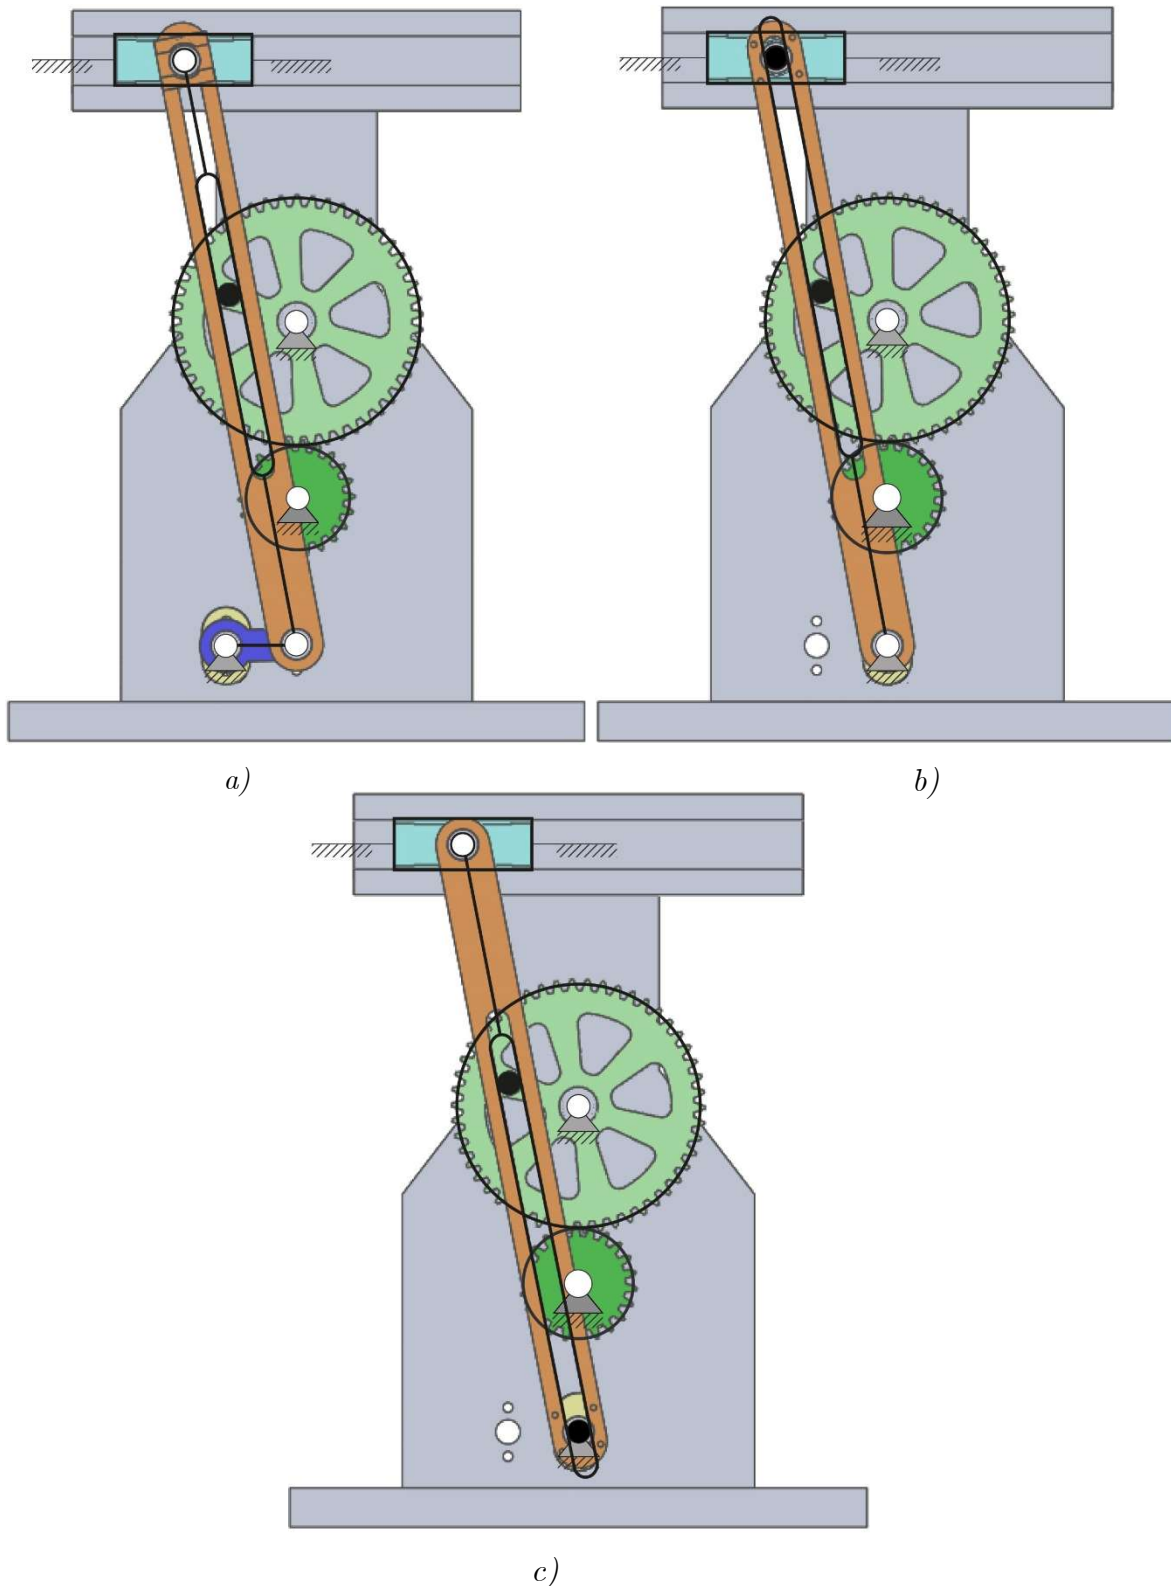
Vistas en alzado de los modelos virtuales de las variantes constructivas con los esquemas de símbolos superpuestos: a) Configuración del mecanismo original, b) Configuración de la segunda variante constructiva y c) Configuración de la tercera variante constructiva.
